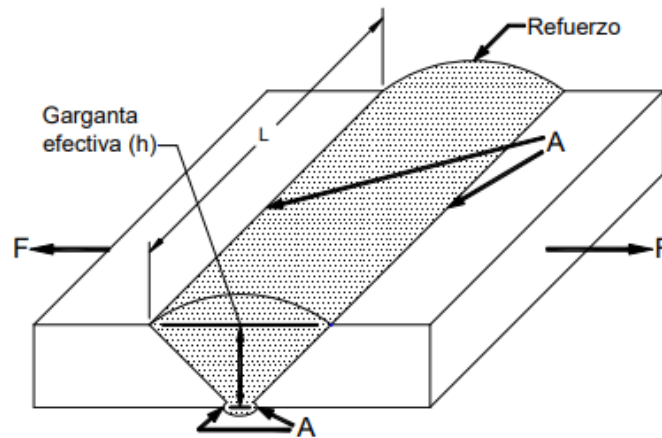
Se muestra la soldadura a tope en una junta [32].
